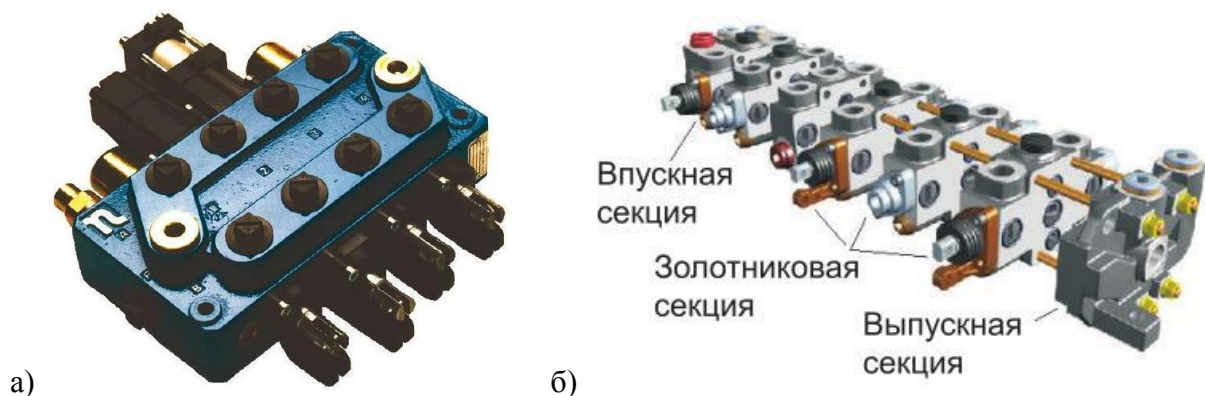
Типы гидрораспределителей по конструкции корпуса:
